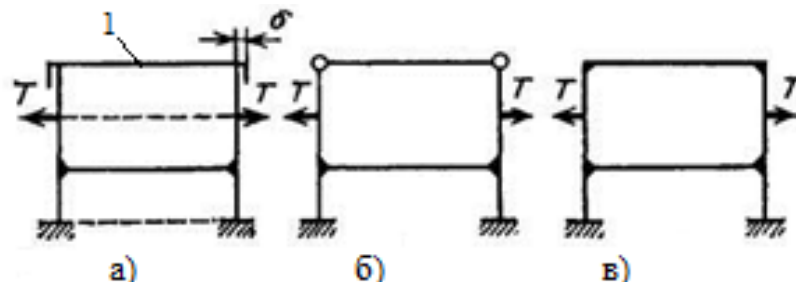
Розрахункові схеми різних конструкцій станин вальців
